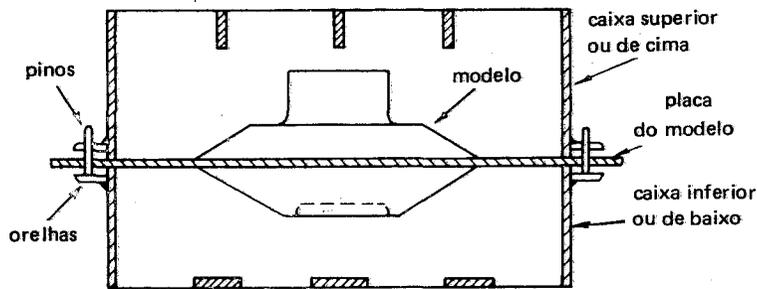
Modelo em placa montada numa caixa de moldar.
